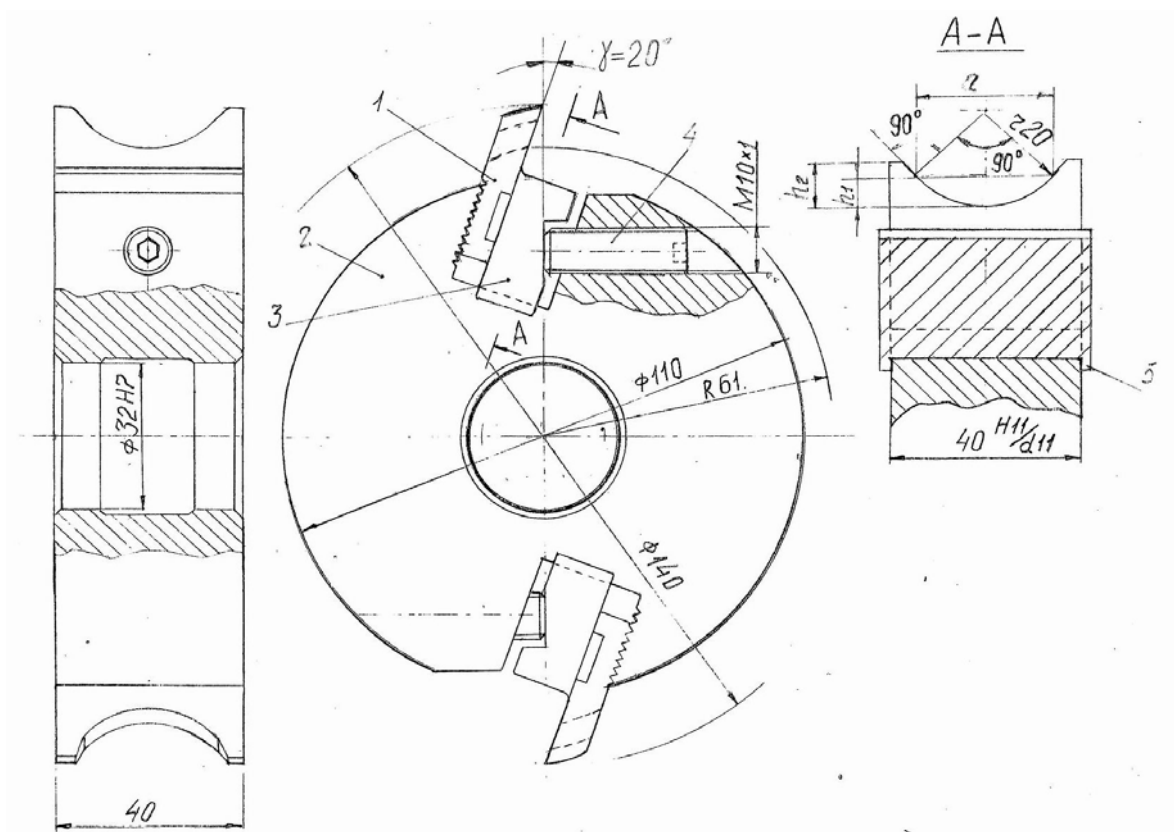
Общий вид сборной фрезы для формирования цилиндрической поверхности
